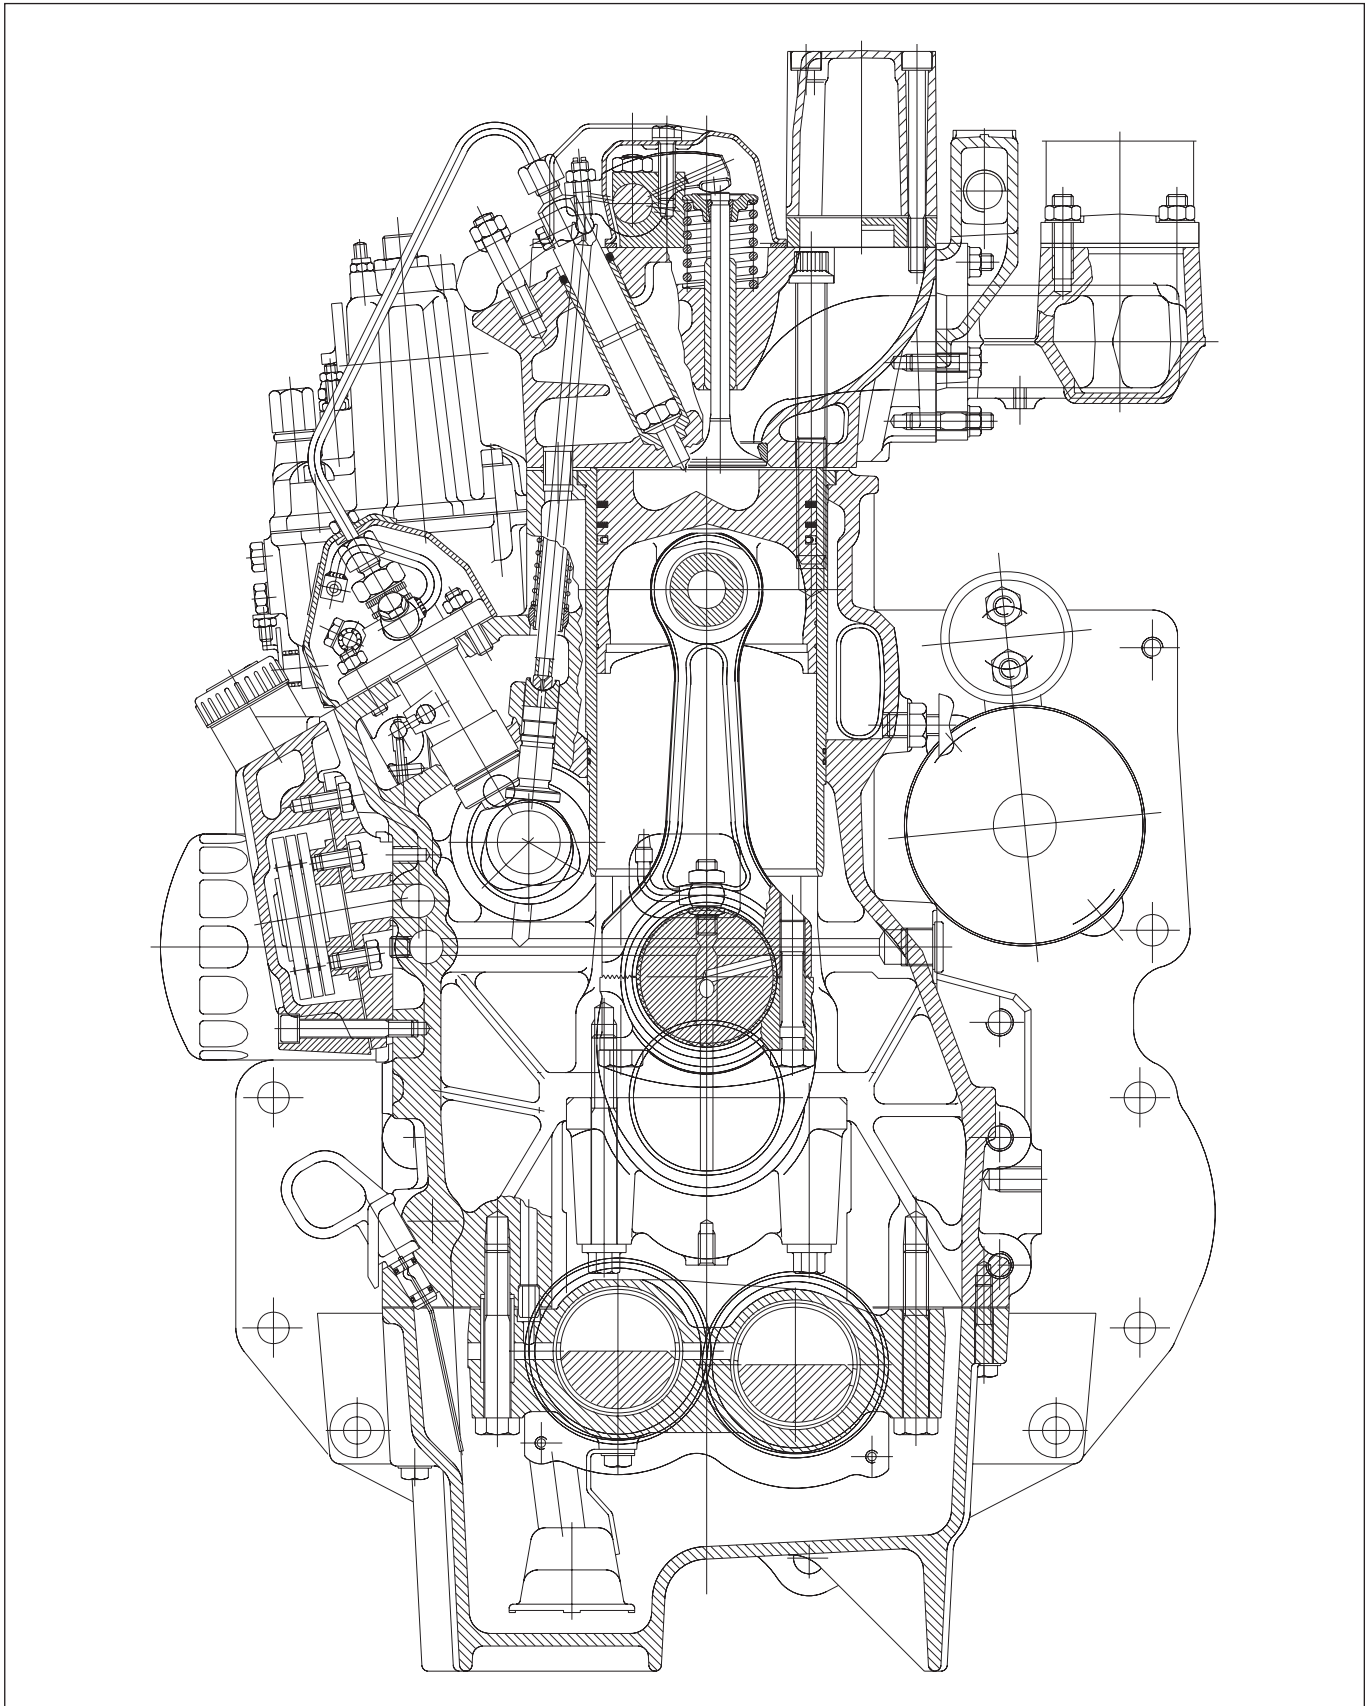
AGROCOMPACT 70F4 - AGROCOMPACT F80 - Coupe transversale du moteur - 4 cylindres.
